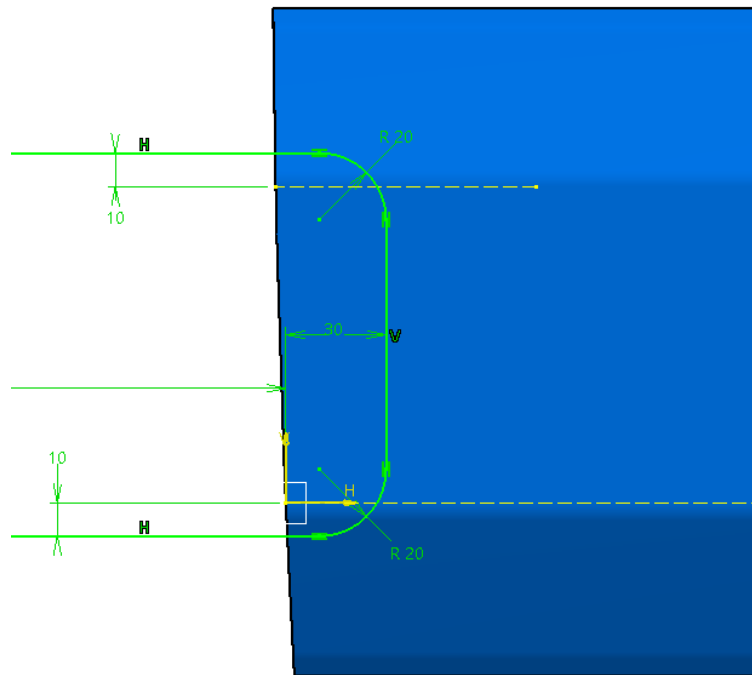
Croquis para el detalle de diseño del embellecedor.
